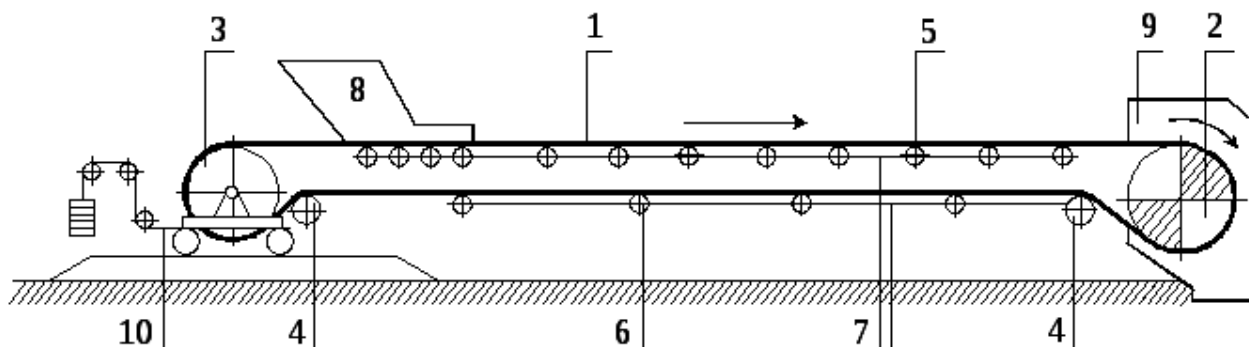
Схема ленточного конвейера: 1 – гибкая лента; 2 – ведущий (приводной) барабан; 3 – натяжной (хвостовой) барабан; 4 – вспомогательные барабаны; 5 – роликковые опоры грузовой ветви; 6 – роликковые опоры порожней ветви; 7 – рама; 8 – загрузочный желоб; 9 – направляющий лоток; 10 – натяжное устройство.
